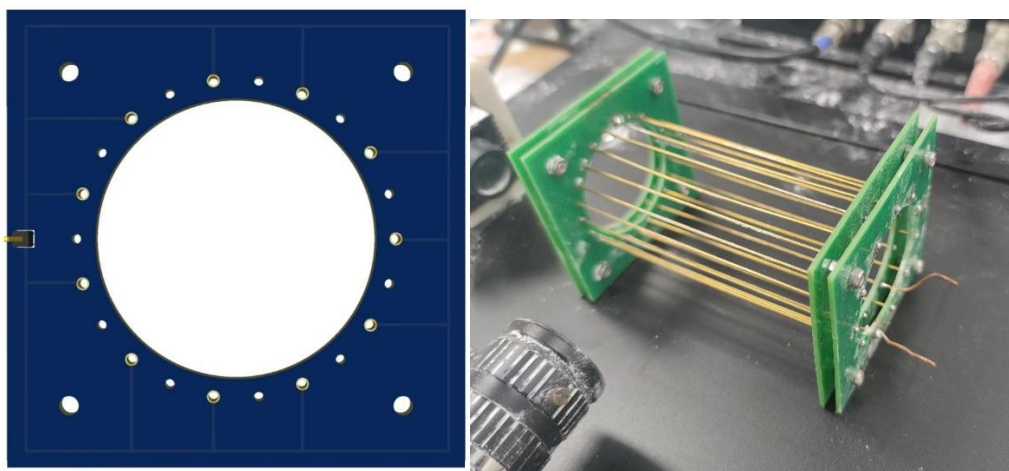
PCB 设计图与装配实物图。左图中两组孔，一组为普通通孔，一组是铜过孔，以实现一组电极导通，一组电极绝缘。右图中以螺栓和螺母保证两组 PCB 的距离保持恒定，以实现机械和电气的稳定性，同时尽可能的减小焊接时热胀冷缩引起的铜棒中应力对于阱几何外形的不良影响。
